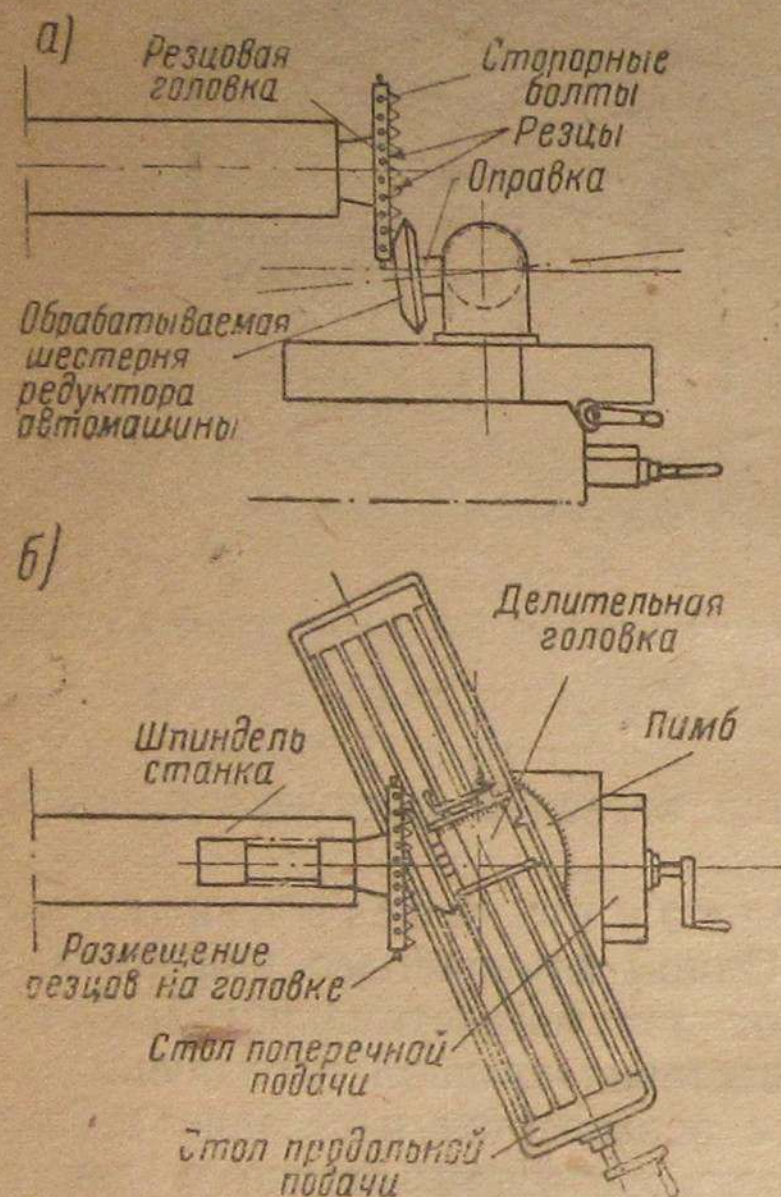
Схема установки обрабатываемой шестерни на станке:
